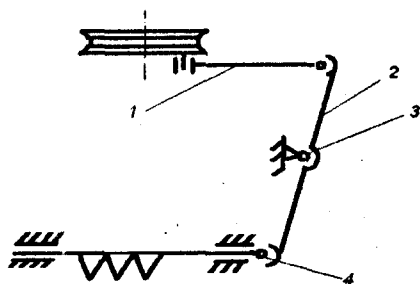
Кривошипно-шатунный механизм с коромыслом:
